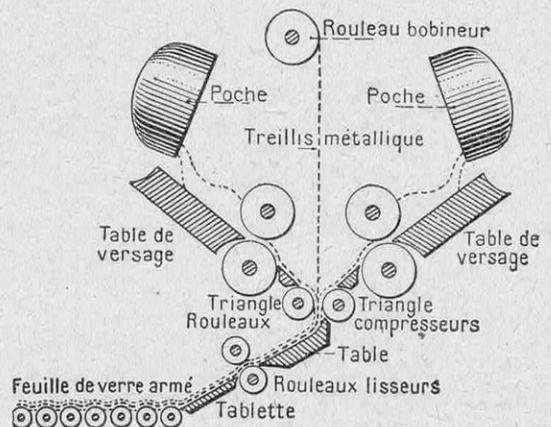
CROQUIS MONTRANT LE FONCTIONNEMENT DE LA MACHINE « UNIVERSELLE »
